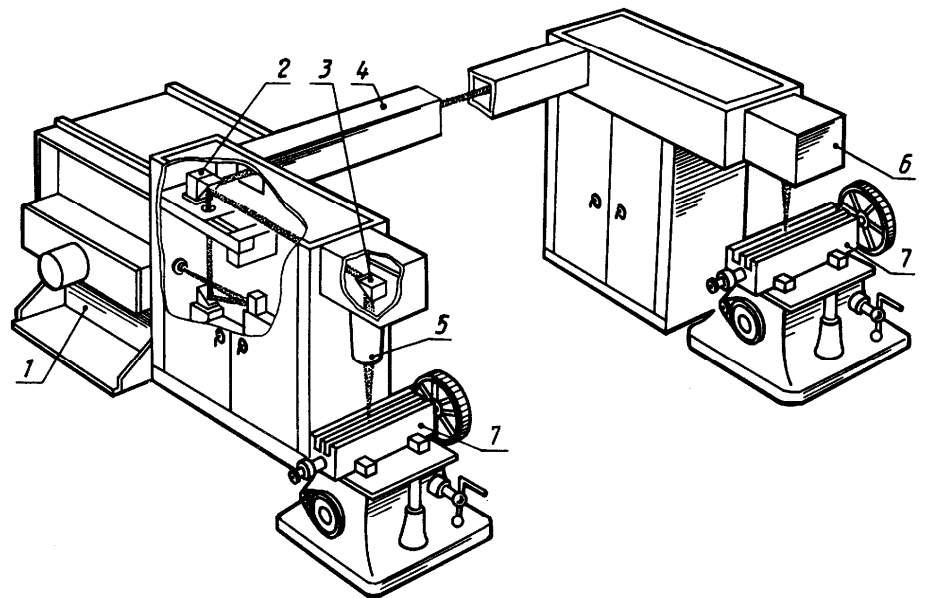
Схема мощной лазерной установки для сварки и термообработки
